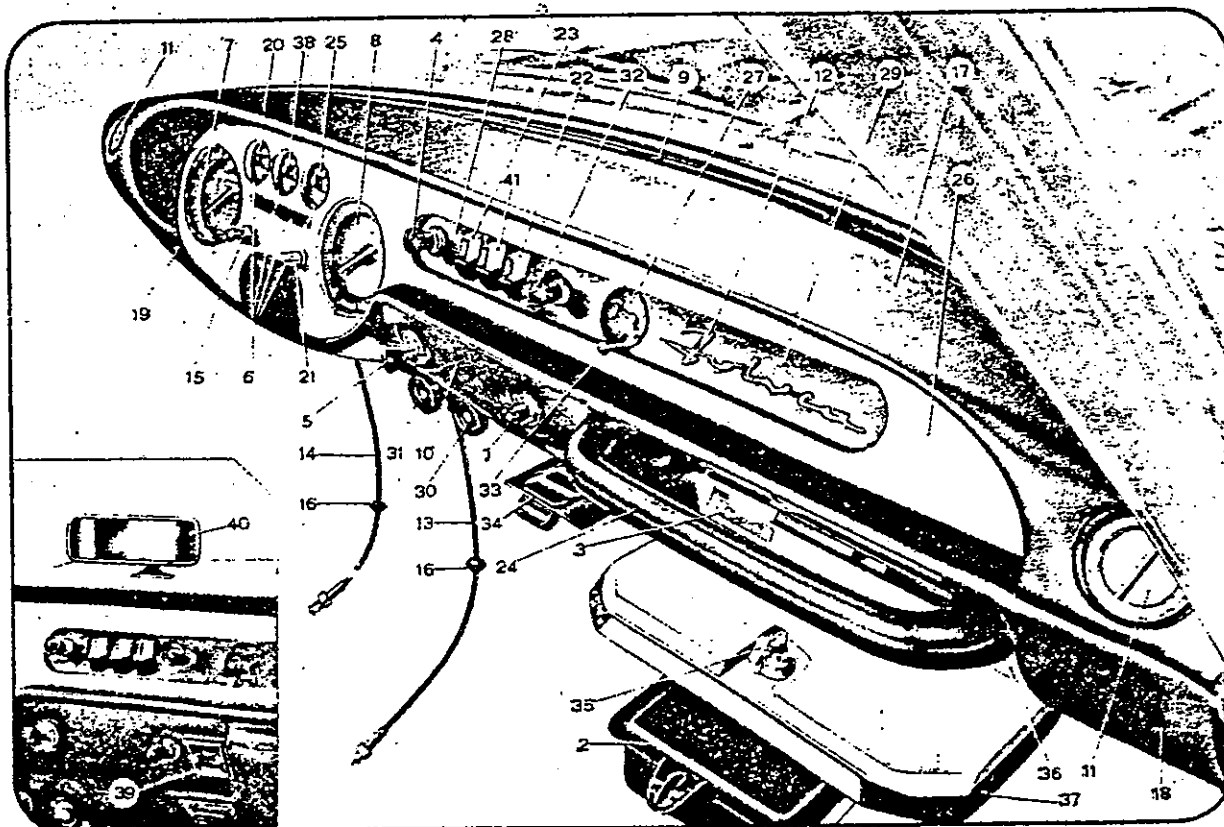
/004 — Equipement planche de bord (Du Catalogue Pièces Détachées)
